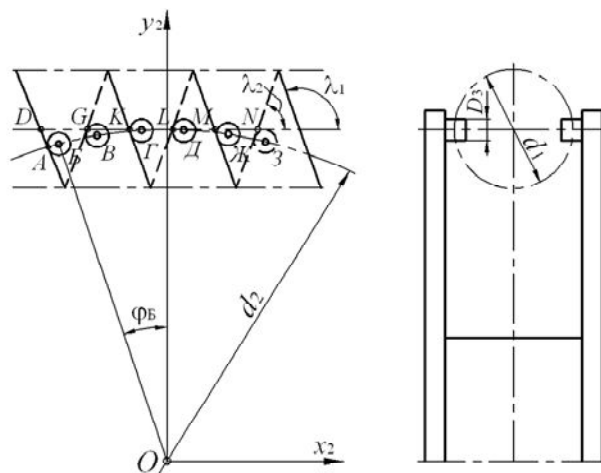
Схема зацеплений пальцев колеса и вращающейся против часовой стрелки пружины с левой навивкой витков
